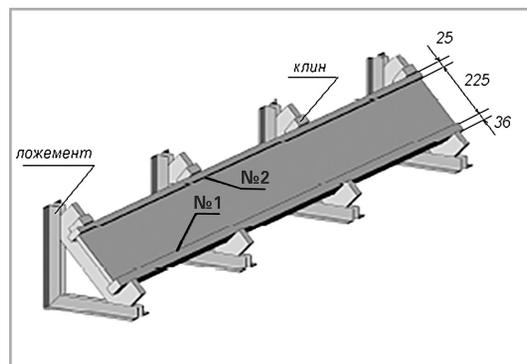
Вид типового сварочного кондуктора для сборки и сварки двутавровых балок
